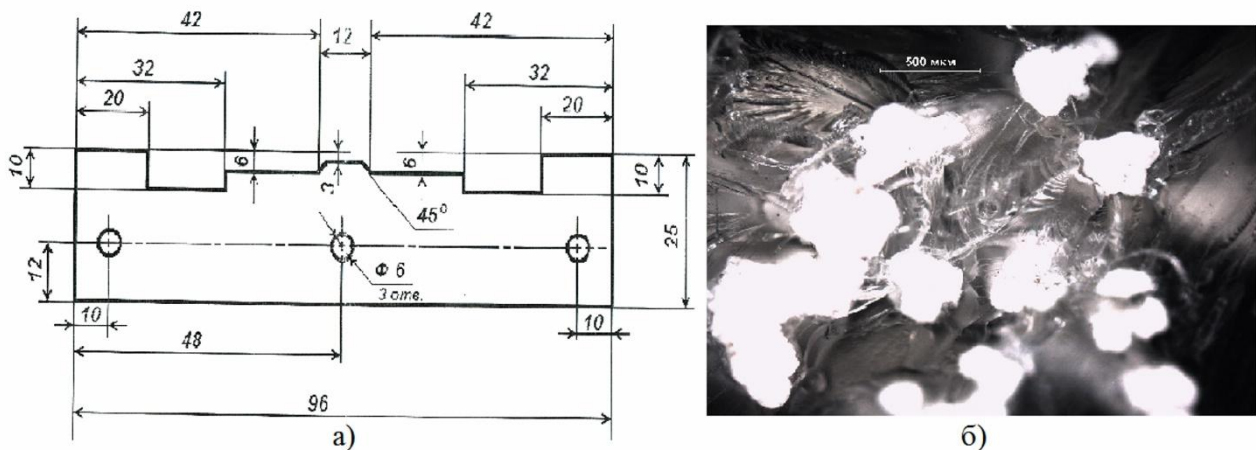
а) – Заготовка для изготовления ячейки для отливки образцов; б) – Фрактограмма излома шейки образца с керамическим волокном
